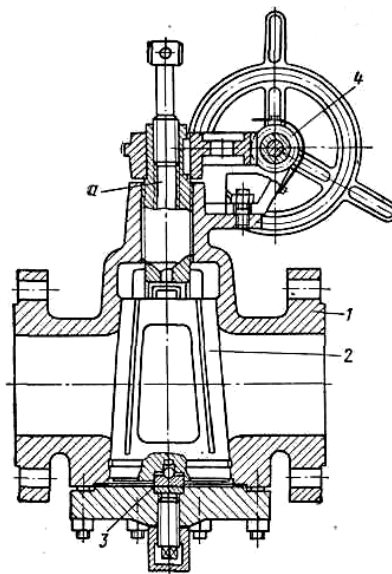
Кран самоуплотняющийся приводной со смазкой: 1 – корпус; 2 – пробка; 3 – шариковая опора пробки; 4 – червячный привод; а – камера для смазки
